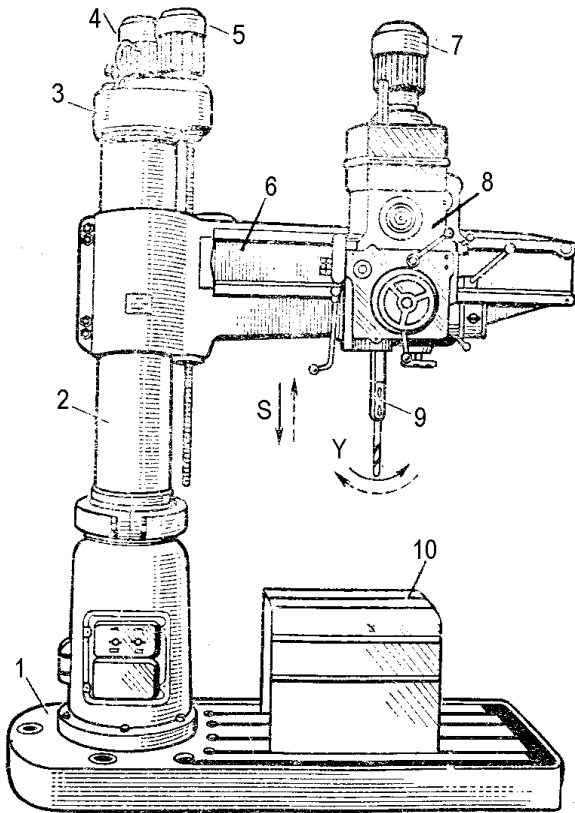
Загальний вигляд радіально- свердлильного верстата
